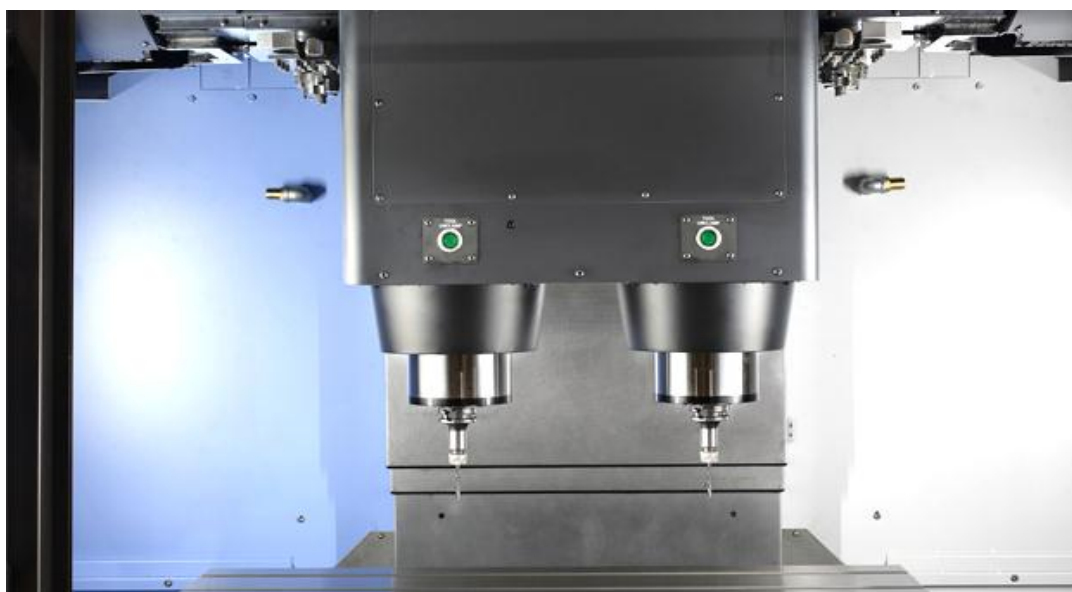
Двухшпindelный вертикальный обрабатывающий центр
